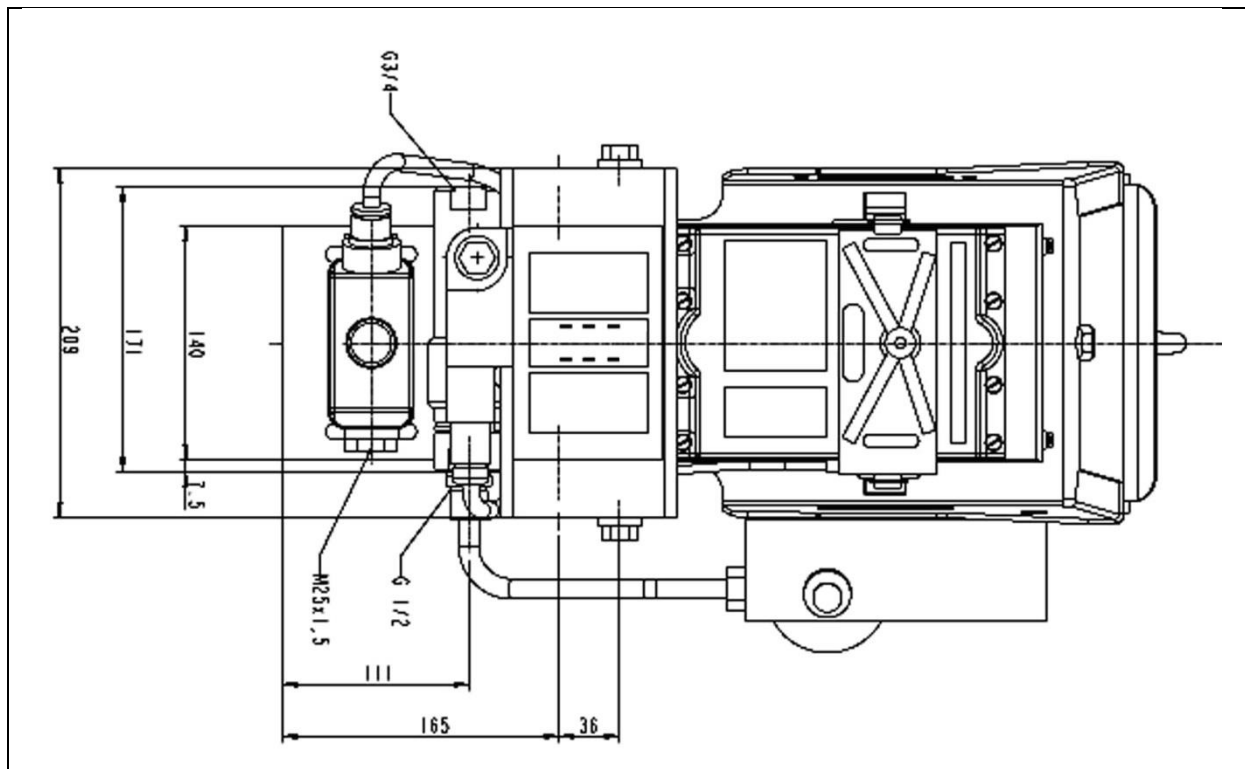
Mechanische Abmessungen des VN116/87plus: Draufsicht
